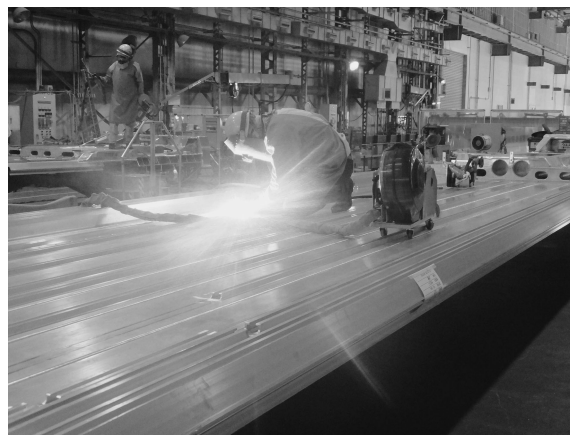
アルミ構体の台枠パネルへの部品取り付けを MIG 溶接で施工
